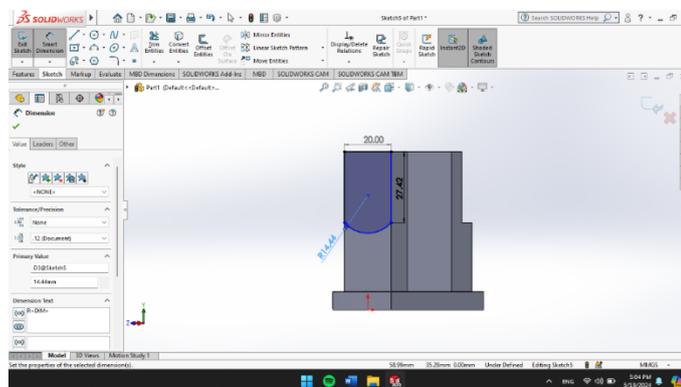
Extruded Cut Sisi Samping Kiri Pada Upper Base
